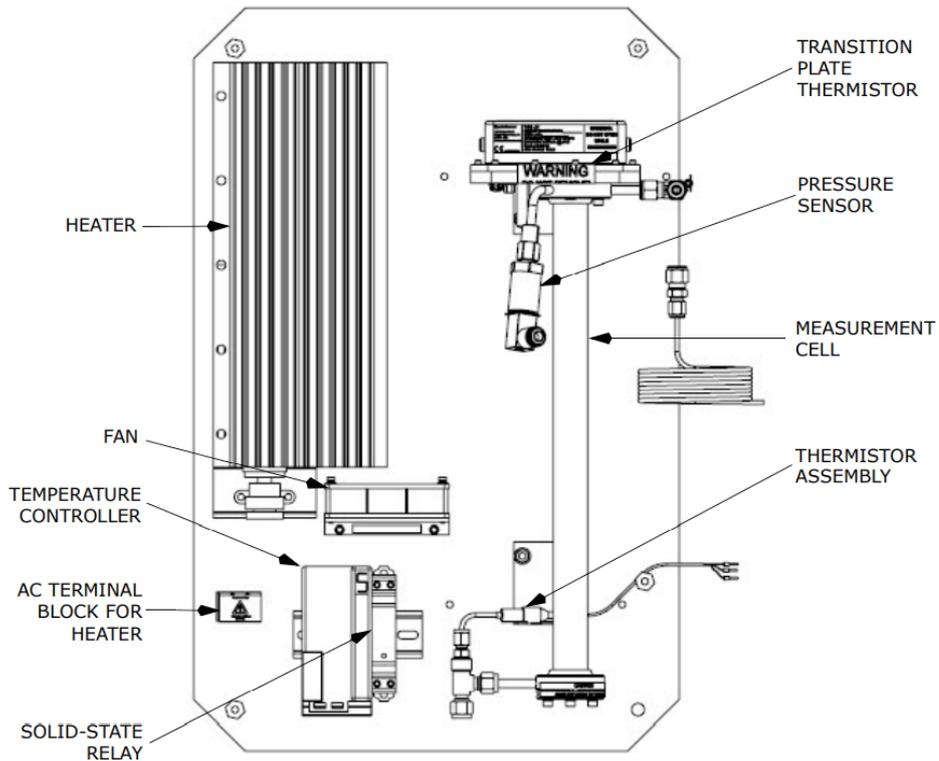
Componentes del conjunto del panel de la celda de muestra (celda de muestra de 0,8 m) (nivel inferior)
